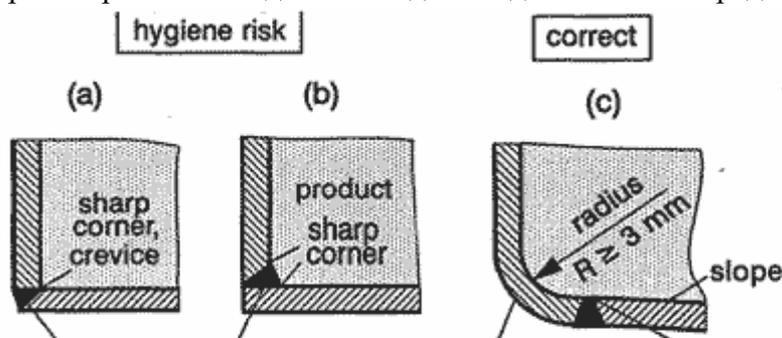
Сварное угловое соединение. (а), (б) Сварные швы в острых углах соединяемых деталей создают негигиеничные области; (с) сварные швы деталей с радиальным углом - гигиеничны.
